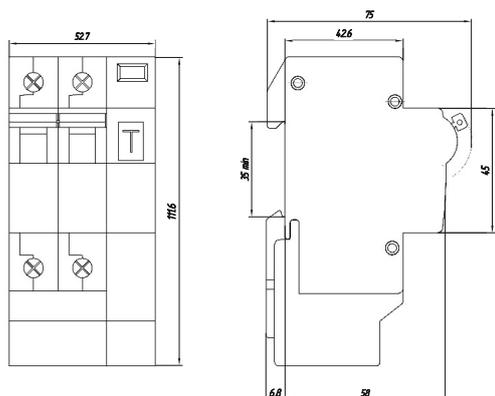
Габаритные размеры «УЗО-ЭЛТА-2Д»
